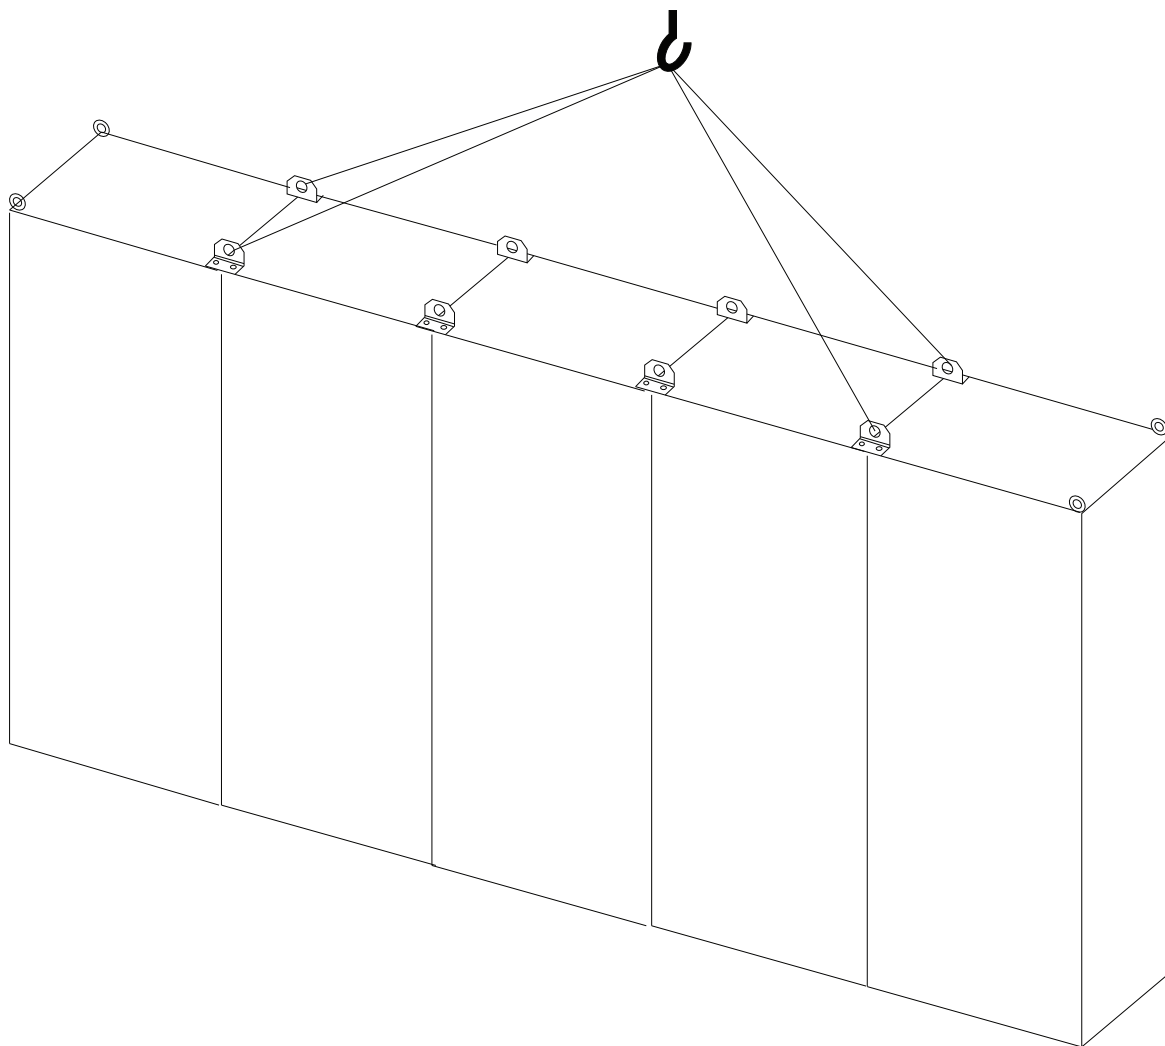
Рекомендуемый способ подъема, размер корпуса F15
